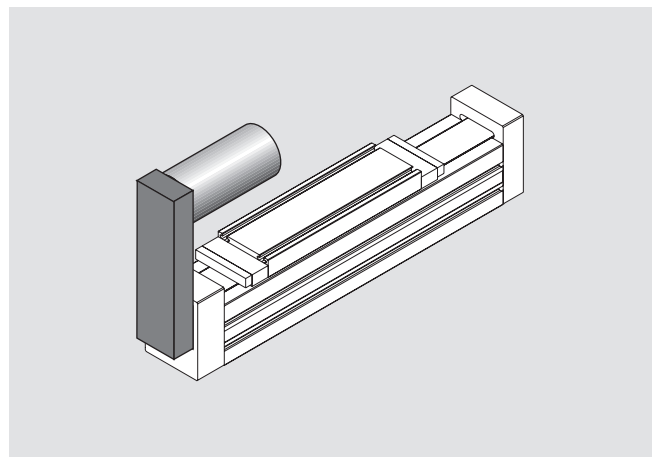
Spindeltrieb mit seitlichem Motoranbau oben (Montagezustand 06)
